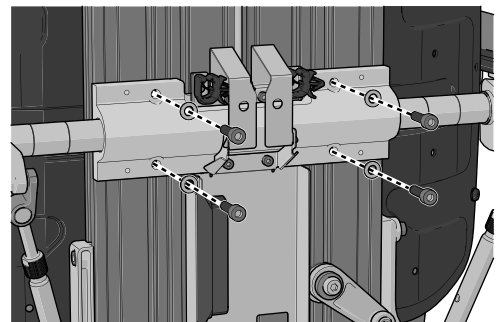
Die Armlehnen sind mit vier Schrauben befestigt.
